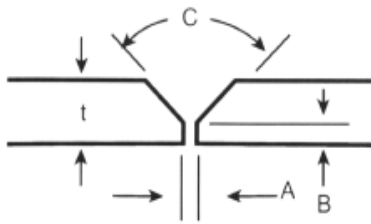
Preparación de la junta en las muestras para la soldadura
